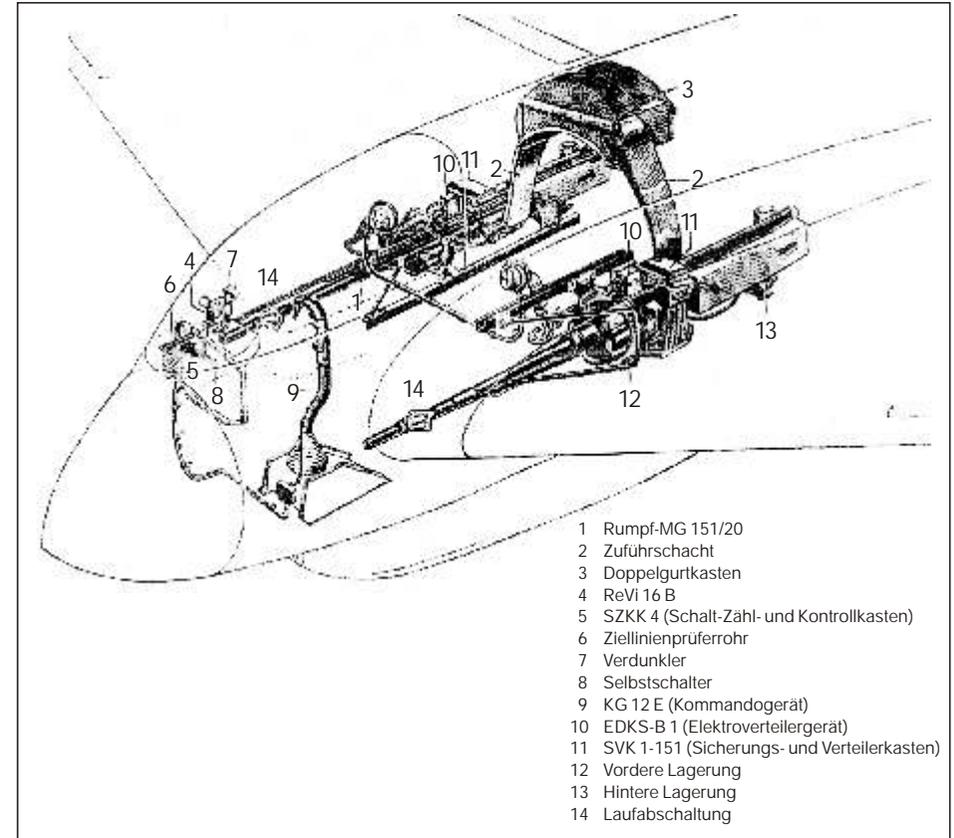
Die Bewaffnung der ersten 45 Stück der Baureihe Me 163 B „Komet“ bestand aus 2 MG 151 / 20 mm. Alle weiteren Maschinen der Baureihe wurden mit MK 108 (30 mm) ausgerüstet.
